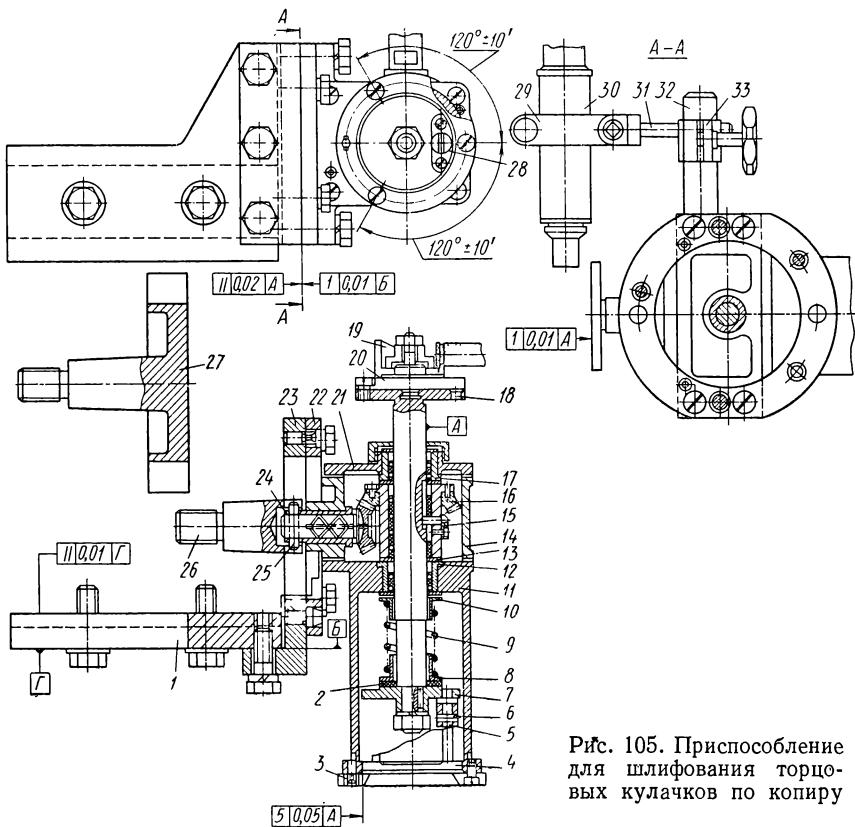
Приспособление для шлифования торцовых кулачков по копиру
